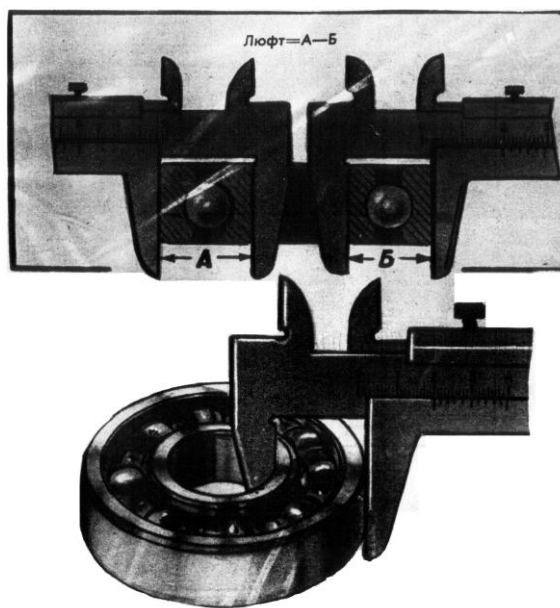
Схема измерения радиального зазора подшипника штангенциркулем.
